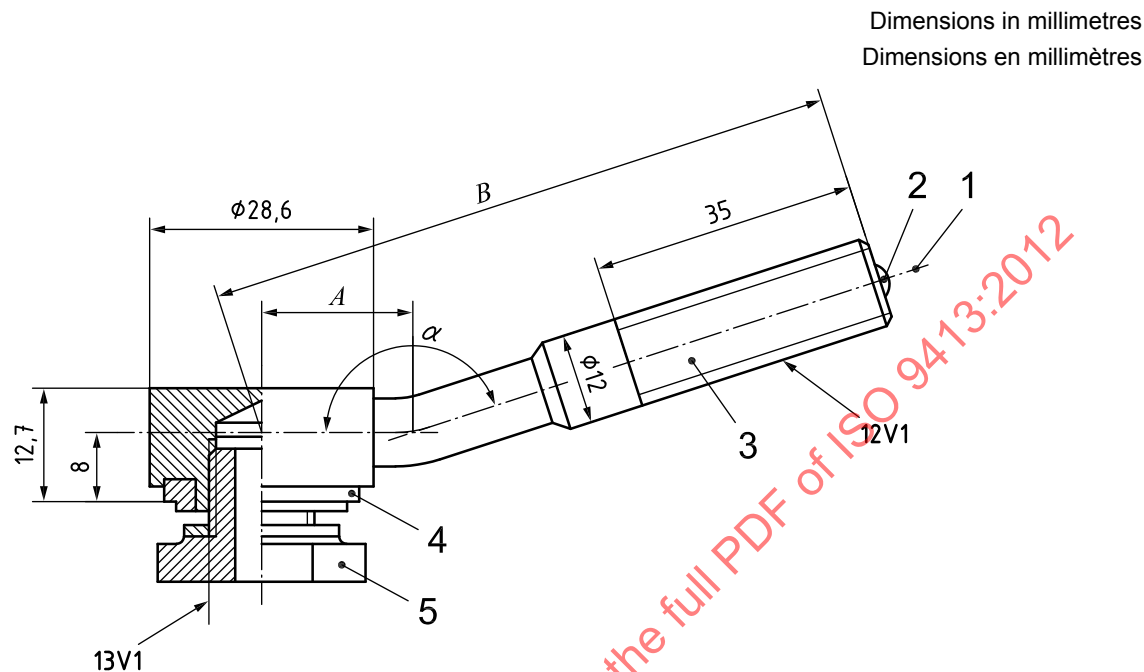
Montage de la valve tubeless air/liquide pour trou de valve pour la jante  $15,7^{+0,4}_0$
